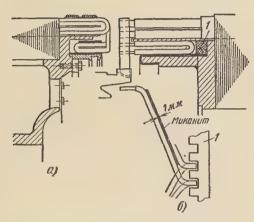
Размещение уравнительных соединений в цилиндрической поверхности.
